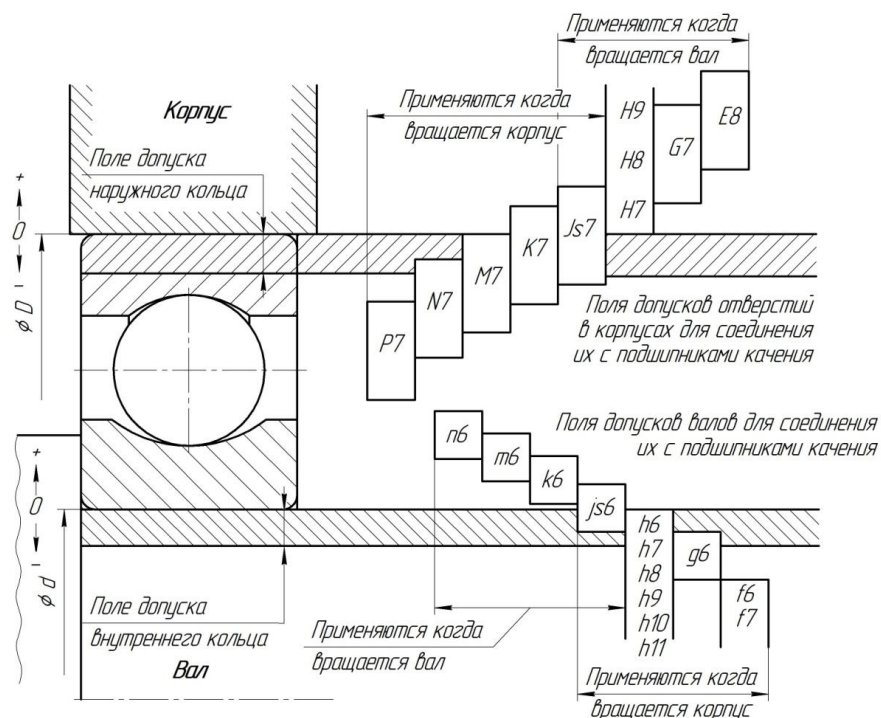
Расположение полей допусков в соединениях «подшипник-вал», «подшипник-корпус»
